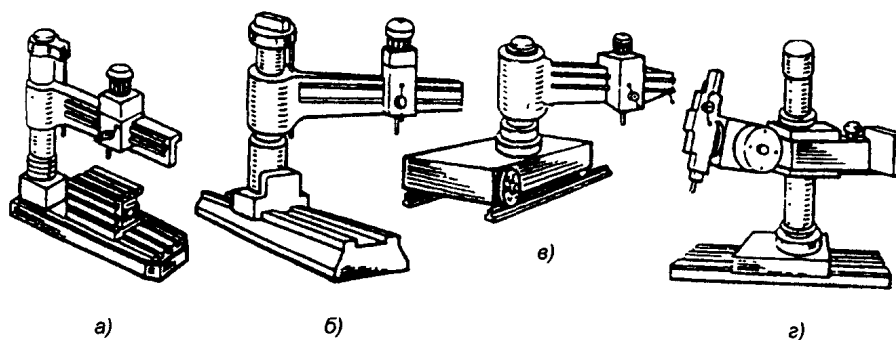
Типы радиально-сверлильных станков: *a* — стационарный общего назначения; *b* — с колонной, перемещающейся по направляющим станины; *в* — передвижной по рельсам; *г* — переносной
